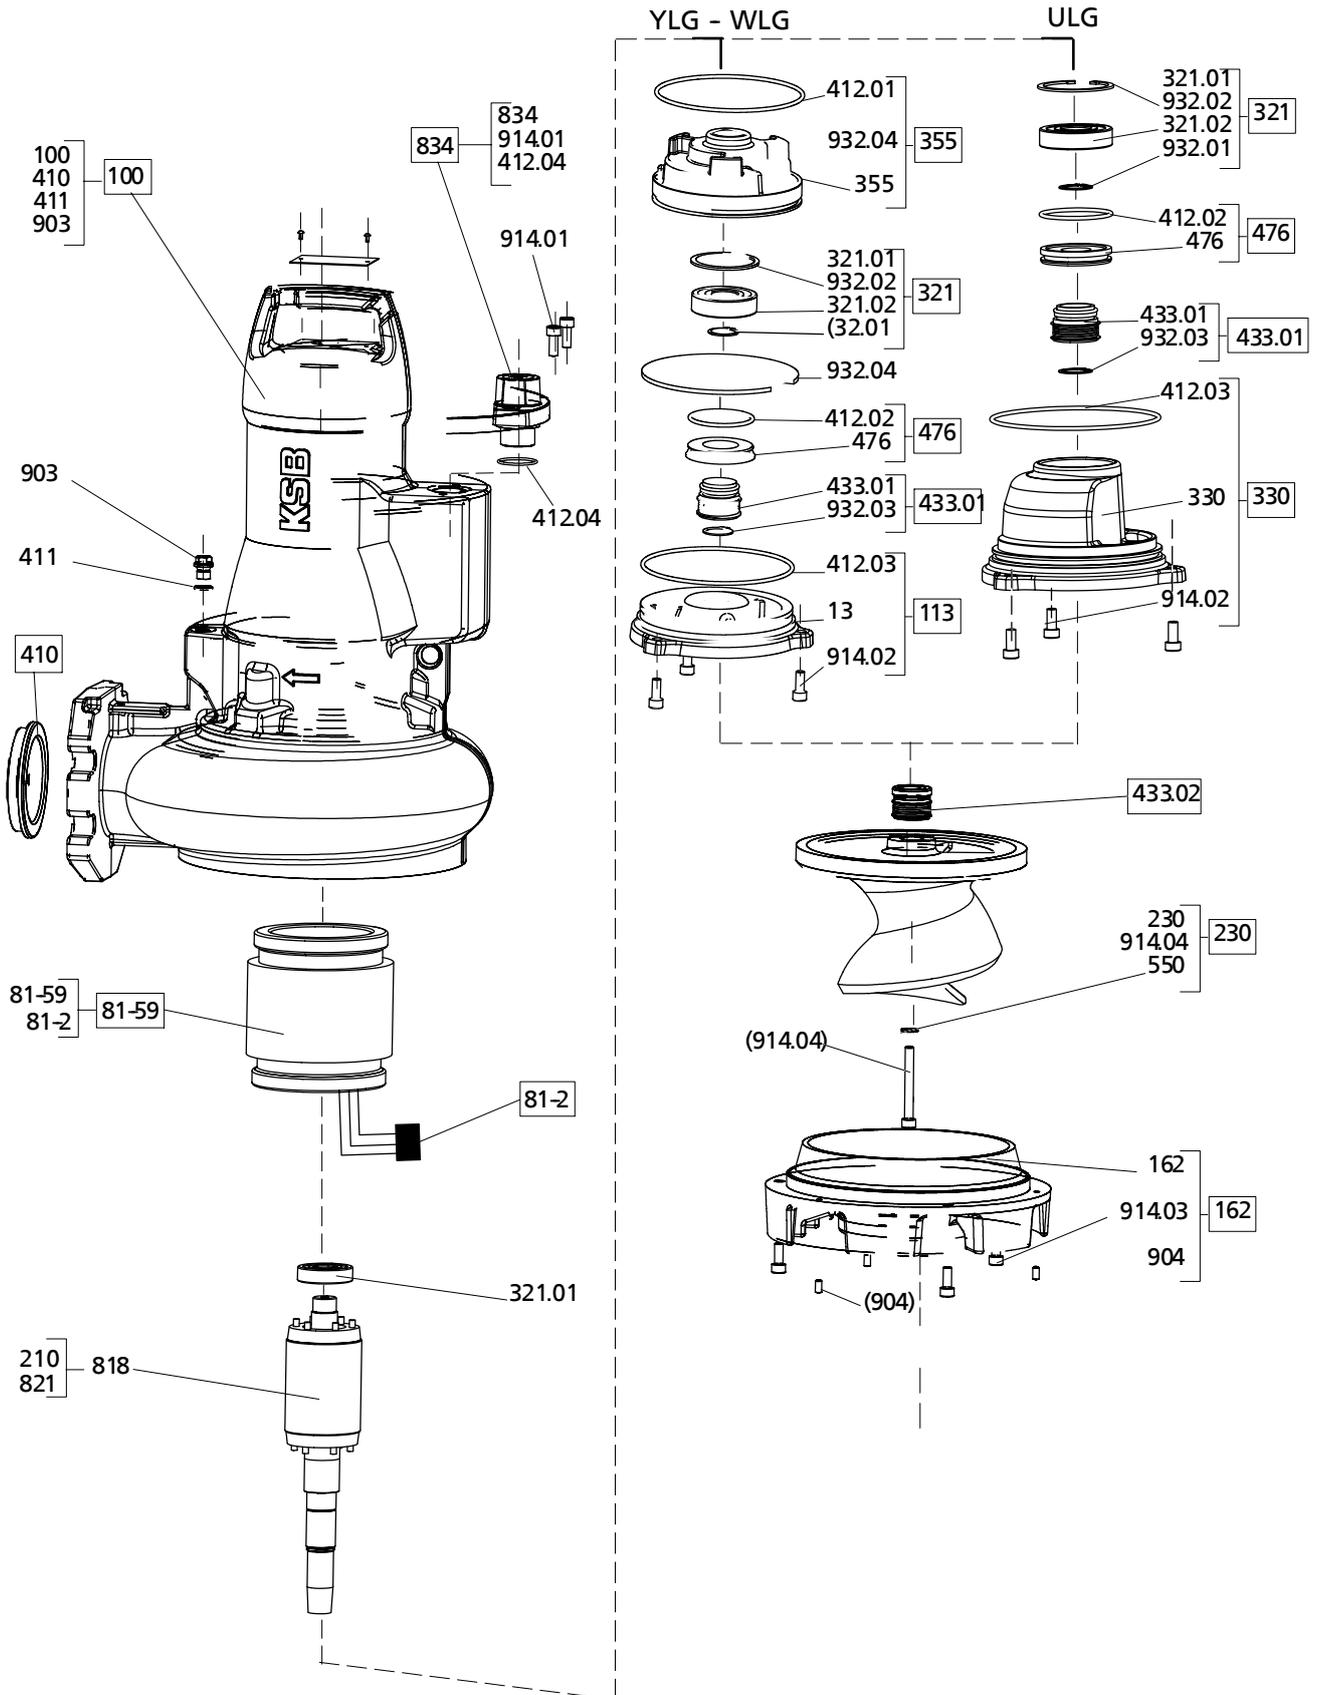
Explosionszeichnung Amarex N mit D 80-100
